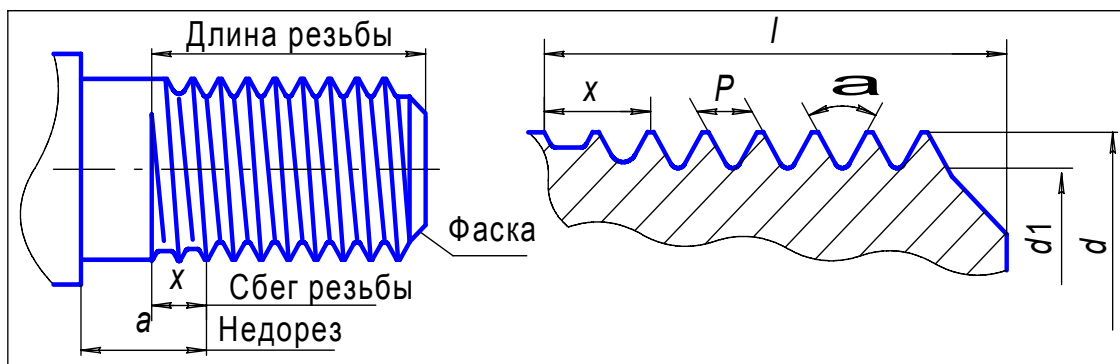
Конструктивные элементы и параметры цилиндрической резьбы
